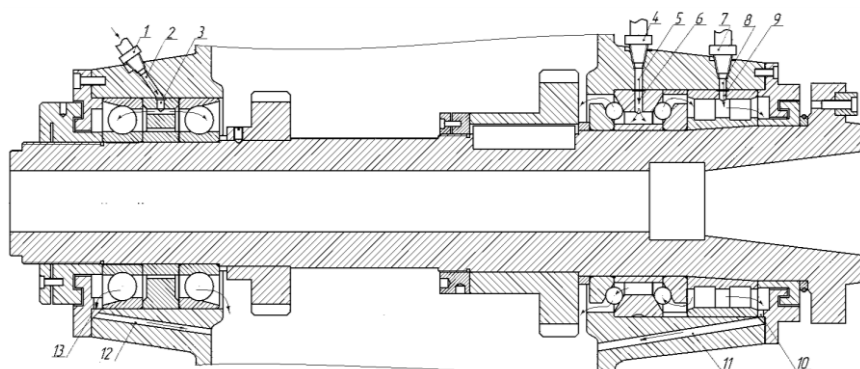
Шпиндельный узел с каналами для циркуляционного смазывания подшипников шпиндельных опор
